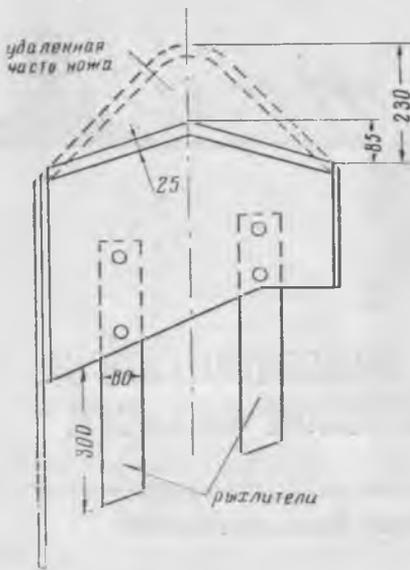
Изменение конструкции выкопчного плуга (вид сверху).
